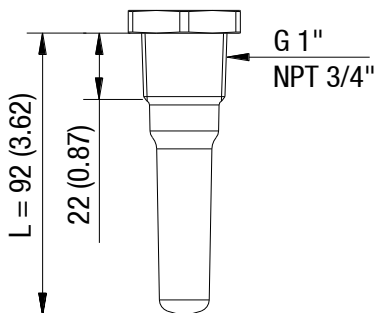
Abmessungen Schutzhülse für Typ CN 7120
